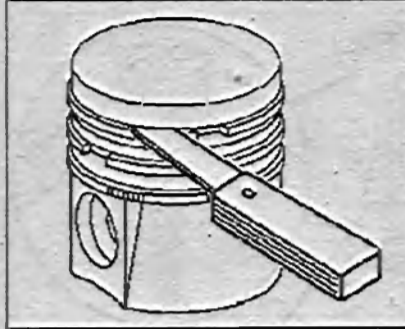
Проверка зазора между кольцом и канавкой поршня.
